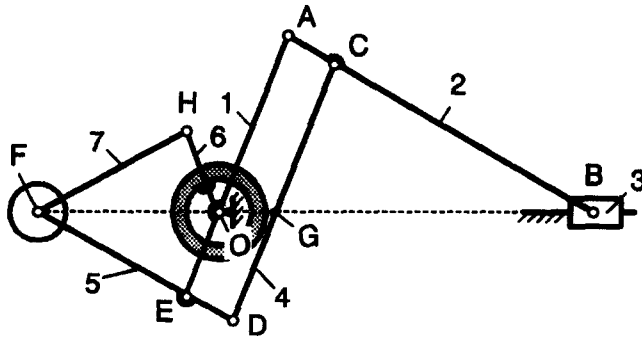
Equilibrage dynamique complet du mécanisme sans engrenages.
